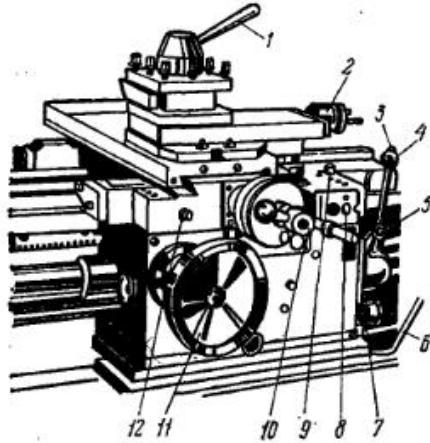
Общий вид и органы управления суппорта станка 16К20:
